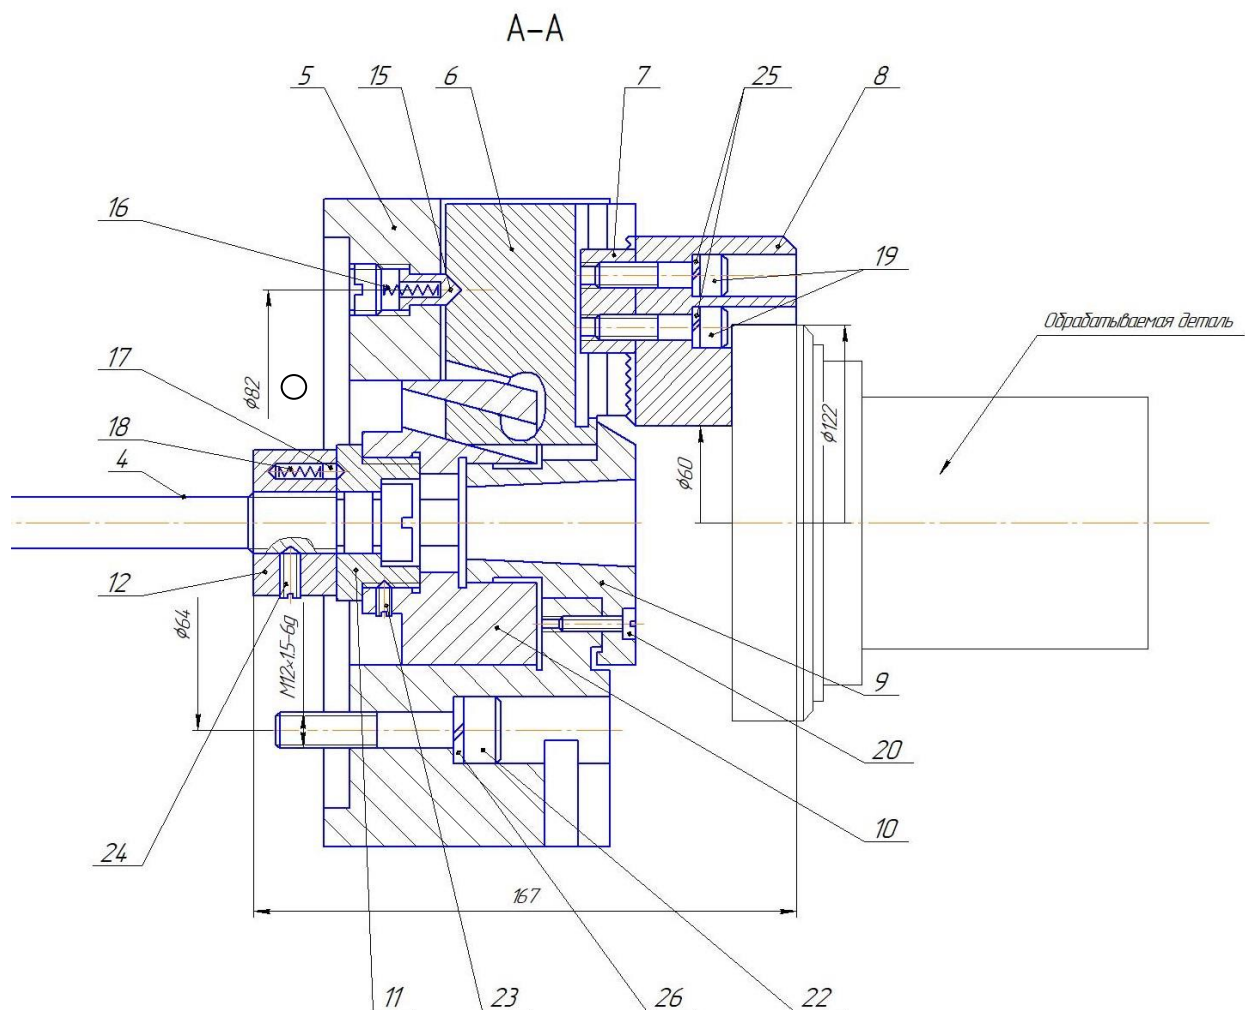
Токарный трёх кулачковый клиновой патрон;
